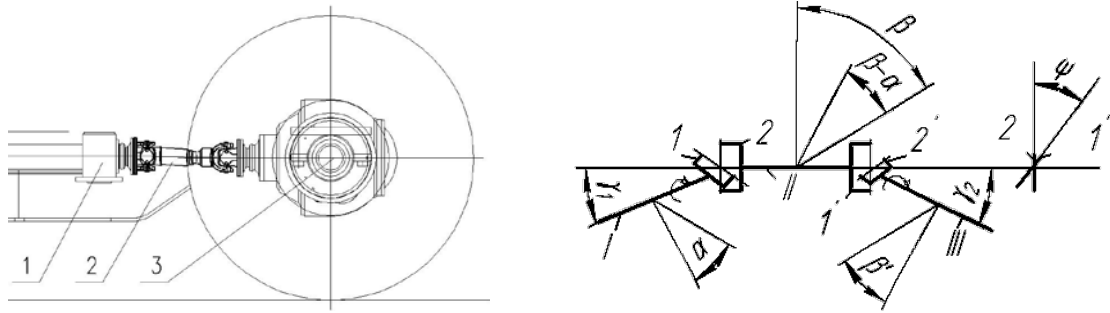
Схема двухшарнирной карданной передачи с обозначением углов:
